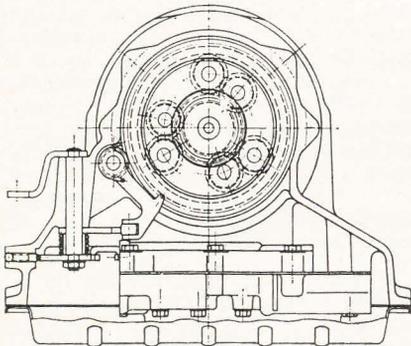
Coupe transversale à la hauteur du train planétaire
